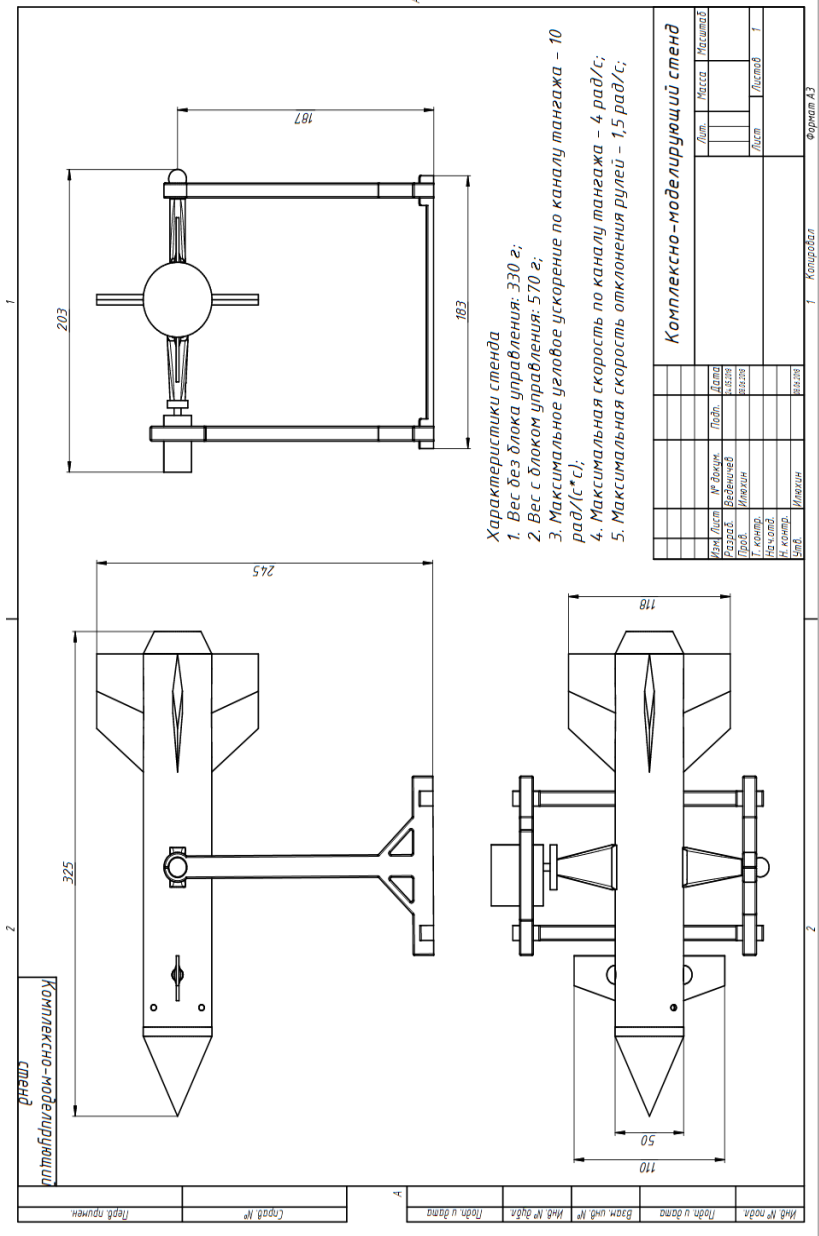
Габаритный чертеж комплексно-моделирующего стенда ЗУР
